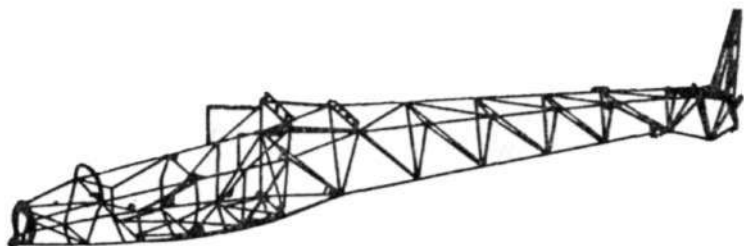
Фюзеляж планера «Пионер», выполненный по ферменной схеме
